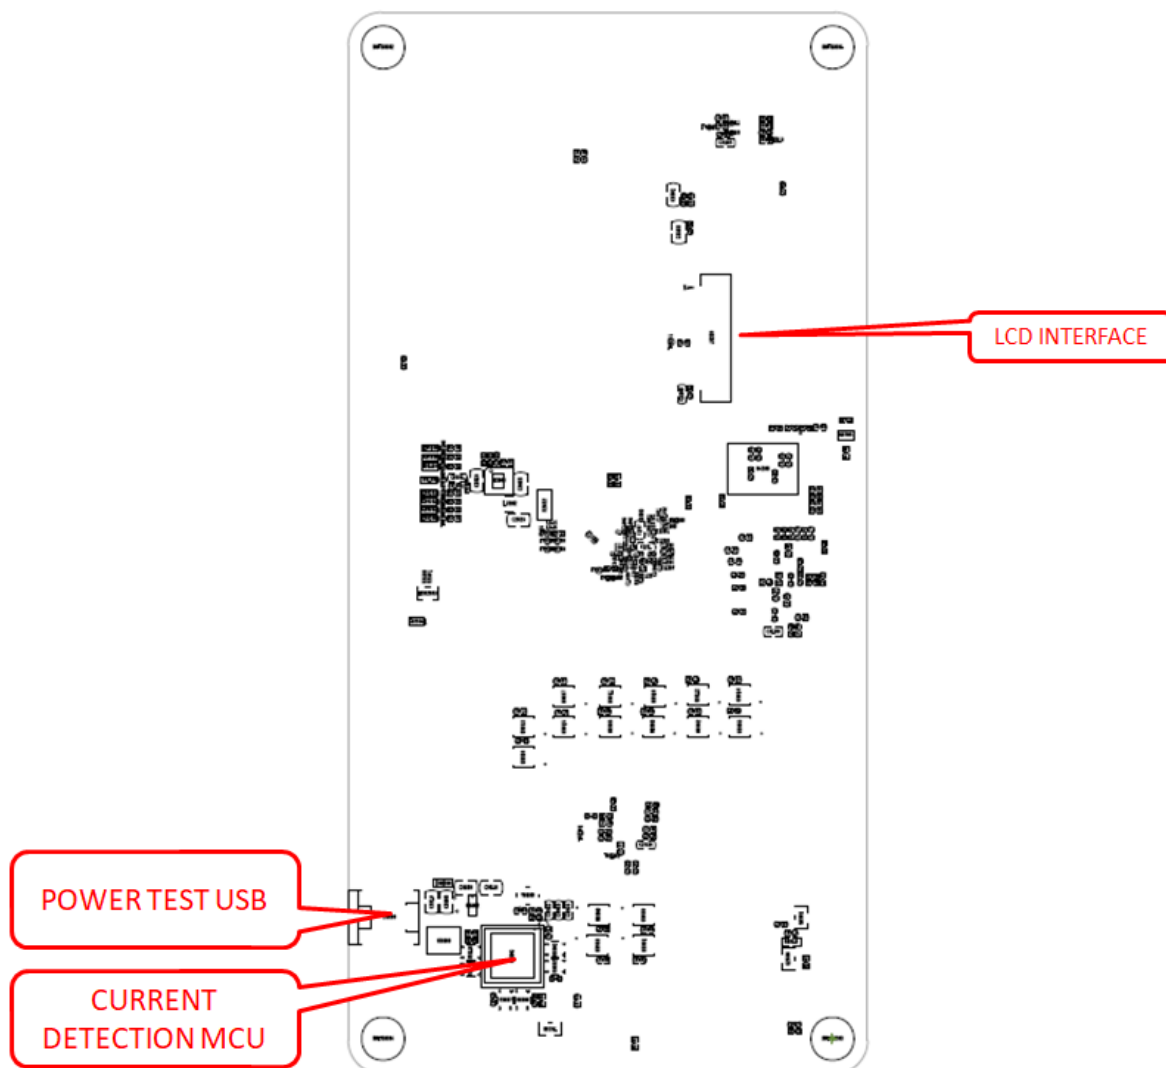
RK1808 EVB 1.1 PCB上bottom Layer模块布局位置图
